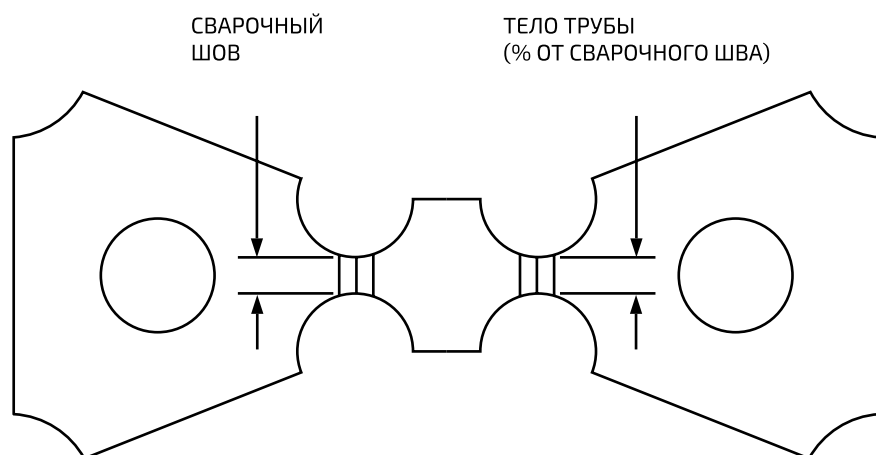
Вид образца для полевых испытаний на мобильном устройстве McElroy
